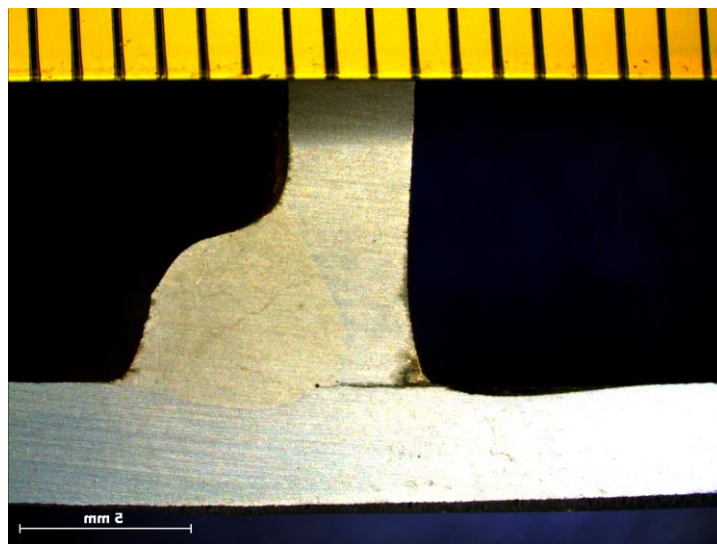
Makroizbrusak uzorka 1. - CV MAG
